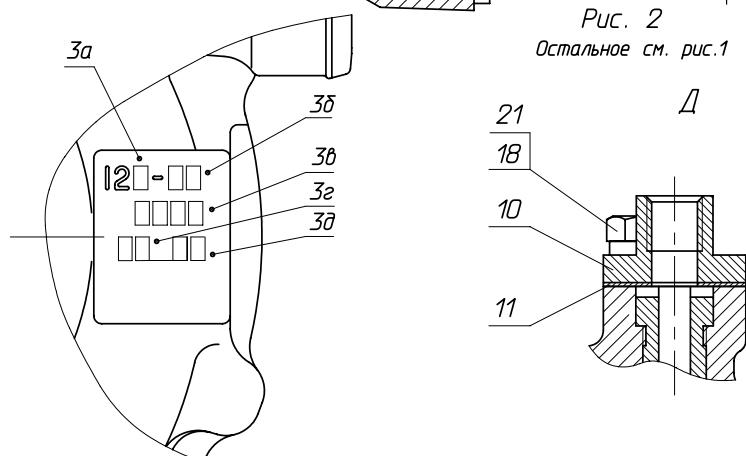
Турбокомпрессор, дет. 122.1118010
